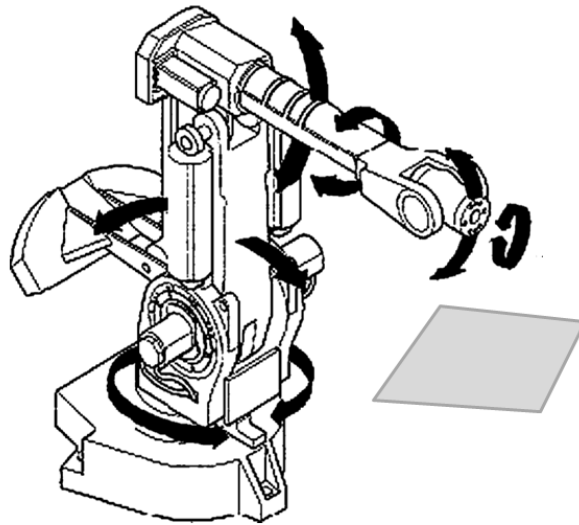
Caso de soldadora sobre placa cuadrada con robot de 6GDL.
